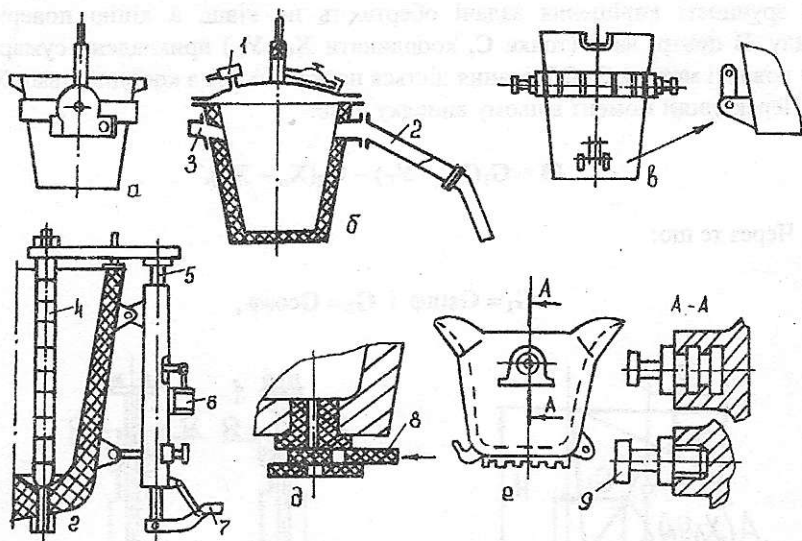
Схеми ковшів для легких металів (а), вакуумного (б), для тяжких металів (в, г, д) і для шлаків (е): 1-вихровий вакуумний насос; 2-хобот; 3-патрубок для зливу металу; 4-стопор; 5-рухомий шток; 6-циліндр дистанційного управління; 7-ручне управління; 8-шибер; 9-цапфи
